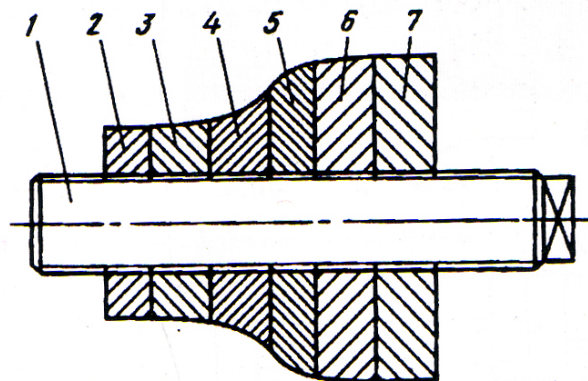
Конструкция пуансона для раздачи концов трубных заготовок
